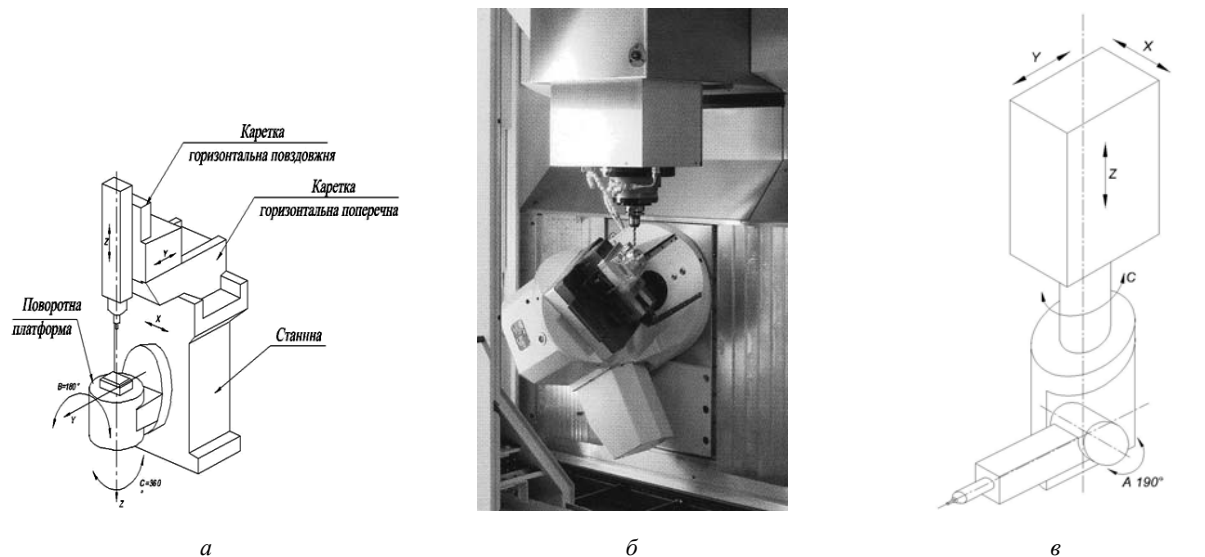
Вертикально-фрезерний консольний верстат із поворотною платформою (столом): а) конструктивна схема, б) фото, в) принципова схема
